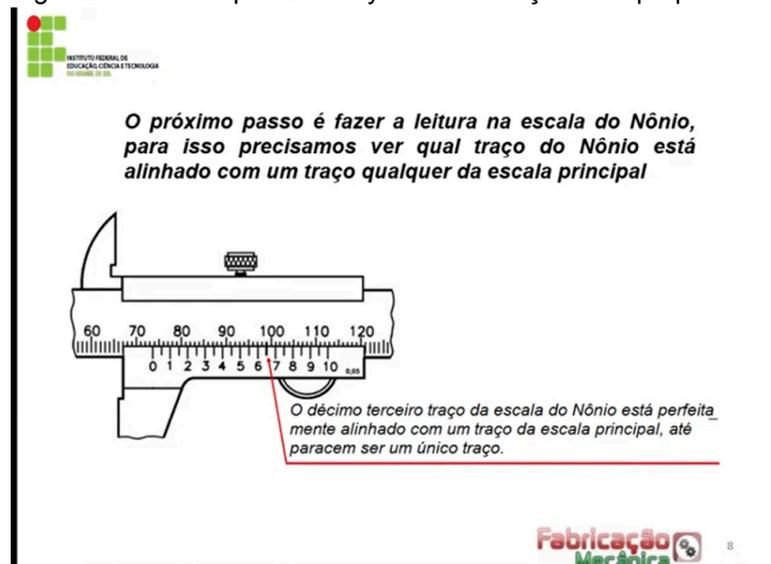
Primeiro vídeo da plataforma youtube medição com paquímetro 0,05 mm
